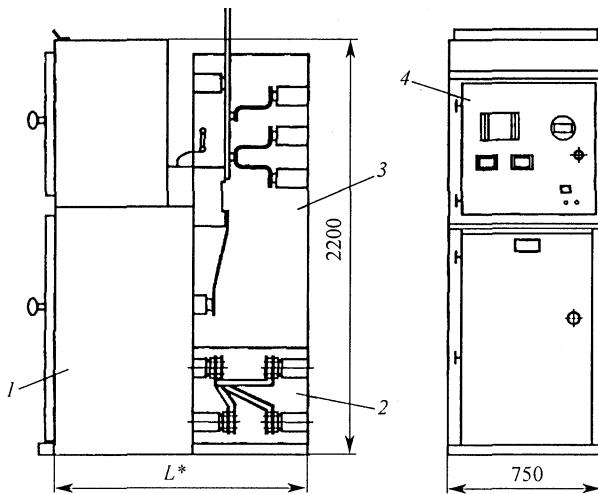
Камера К-104М с выключателем и шинным вводом сверху: 1, 2 — отсеки сборных шин; 3 — линейный отсек; 4 — релейный шкаф
